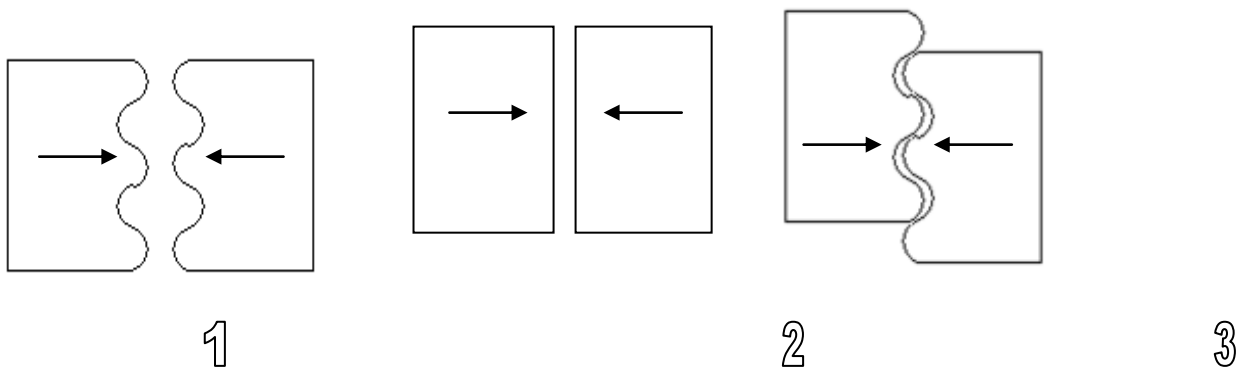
Ejemplo de tipos de sellado: Acanalado y Plano.
